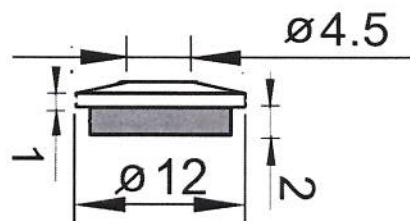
Уплотнительная шайба для резьбовых шпилек X-BT
